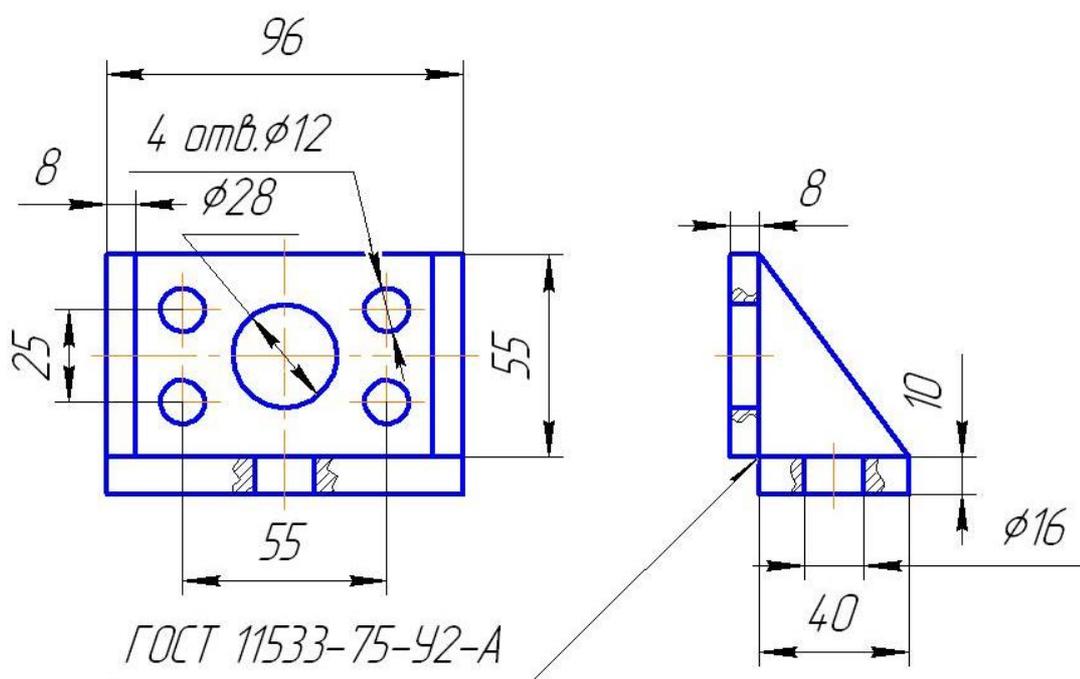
Угловое сварное соединение со швом без скоса кромок, выполненное автоматической сваркой
